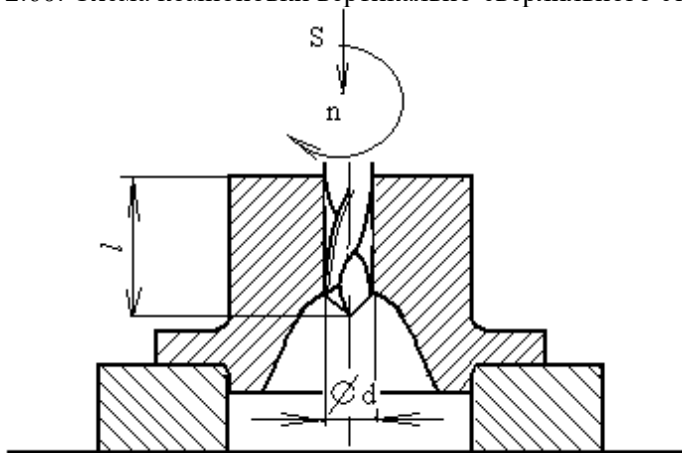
Схема сверления отверстия в заготовке на вертикально-сверльном станке
